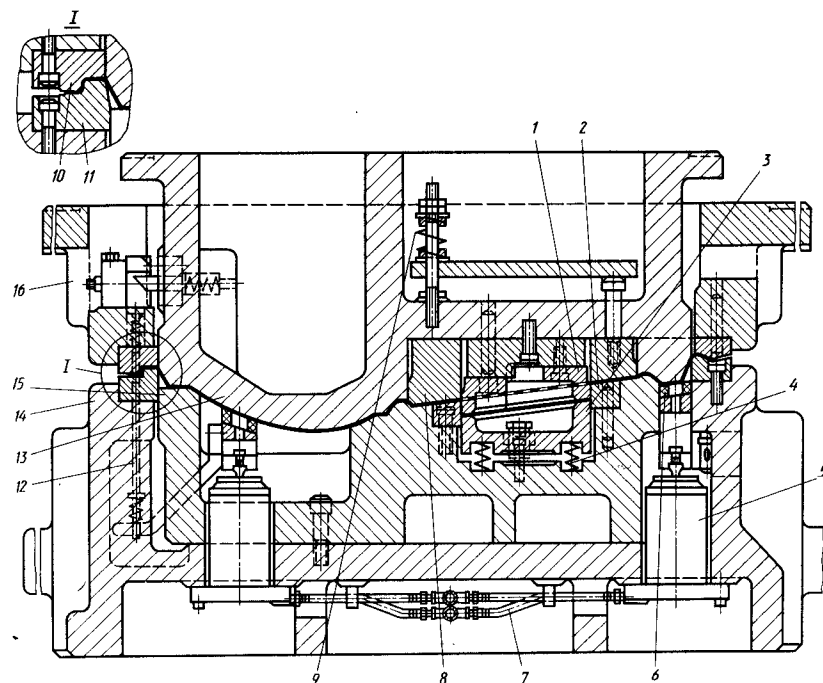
Конструкция крупногабаритного штампа для вытяжки с механизацией подъема штампуемой детали
